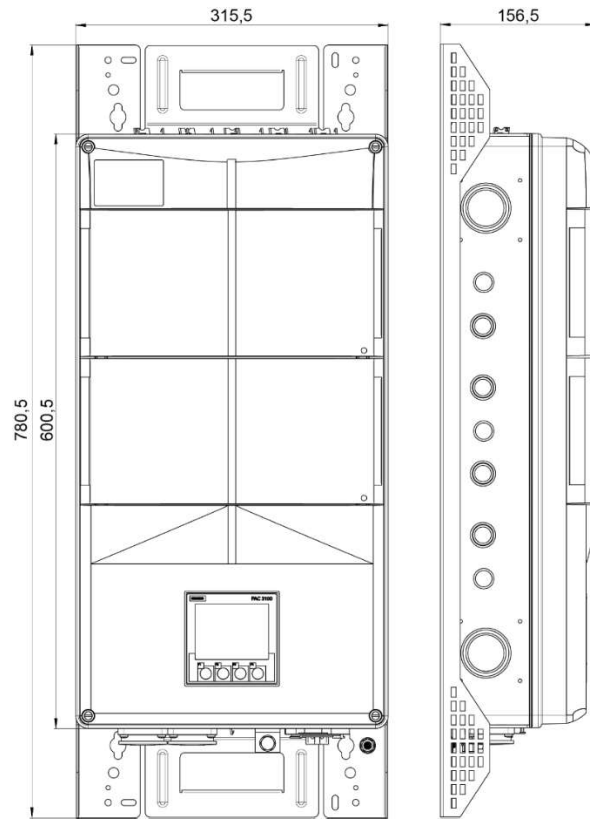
Front- und Seitenansicht gesis® WIV, Höhe 780 mm
